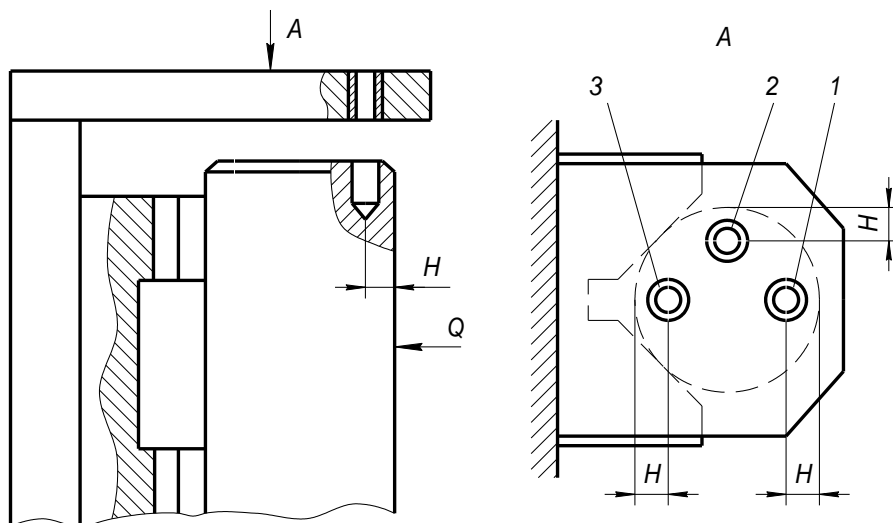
Схемы установки кондукторной втулки при сверлении отверстия в торце вала
